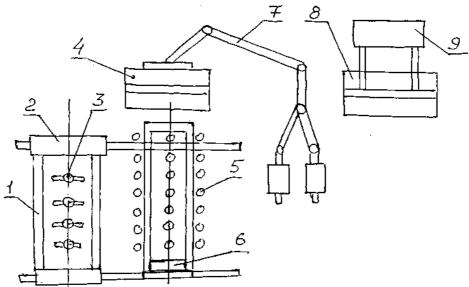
Структурная схема участка (вид в плане) резки листов: 1 - стеллаж; 2 - листоукладчик; 3 - сменные захваты (вакуумные или электромагнитные); 4; 8 - ножницы кривошипные; 5 - рольганг с пневматическими шаровыми опорами; 6 — механизм подачи; 7 - манипулятор со стапелирующим столом; 9 - стапелирующетранспортирующая тележка.
